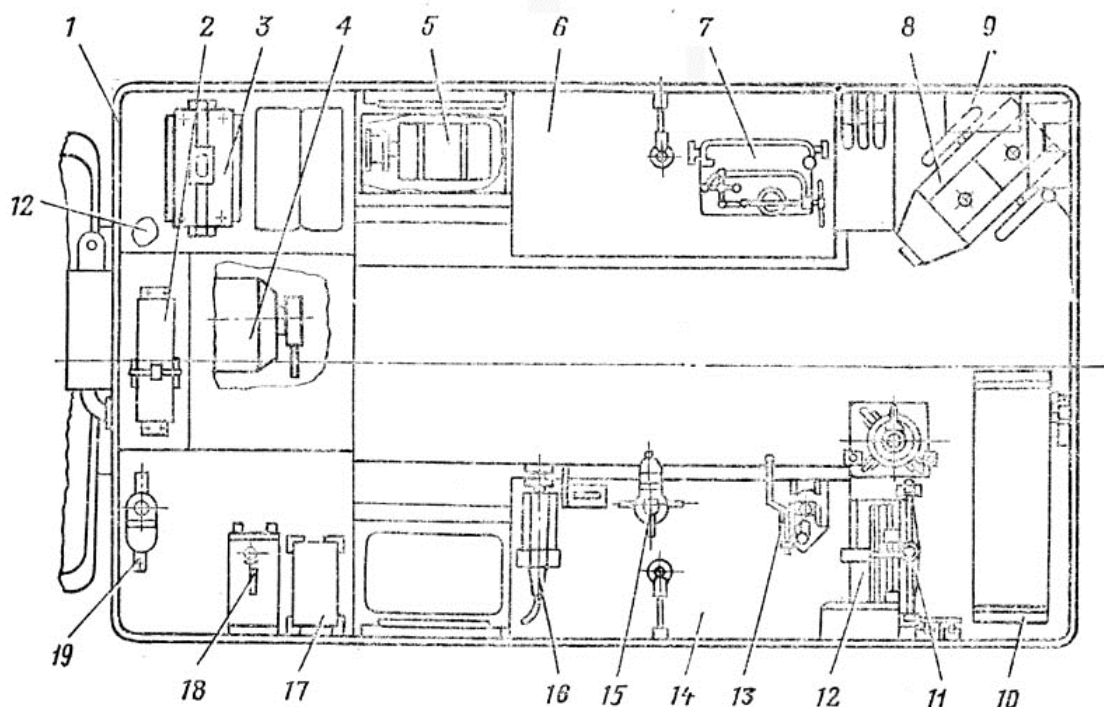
План размещения оборудования в мастерской МРС-АТ: 1 – кузов; 2 – индикаторный нутромер; 3 – прибор для проверки автомобильного электрооборудования; 4 – генератор; 5 – преобразователь частоты тока; 6 и 14 – верстаки; 7 – стенд для проверки форсунок; 8 – сварочный преобразователь; 9 – щит с автоматической защитой; 10 – отопительная установка палатки; 11 – комплект приспособлений и инструмента для ремонта гусеничных тягачей; 12 – выносной стол; 13 – штатив для ручной электросверлильной машины; 15 – слесарные тиски; 16 – электрошлифовальная машина; 17 – радиометр-рентгенметр; 18 – зарядно-разрядное устройство; 19 – бачок для питьевой воды
